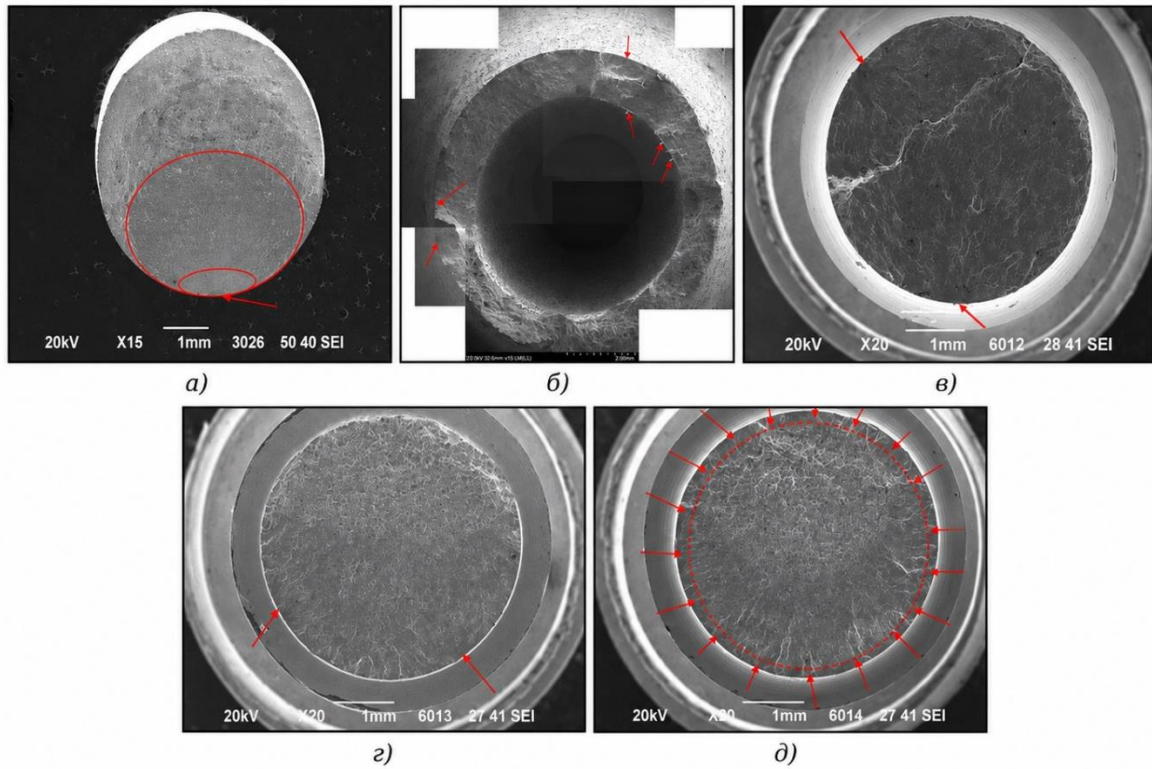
Общий вид поверхности разрушения образцов: а – без концентратора напряжений; б – тонкостенный образец с технологической шероховатостью; в – с надрезом С-типа; г – с надрезом V-типа; д – с надрезом U-типа
